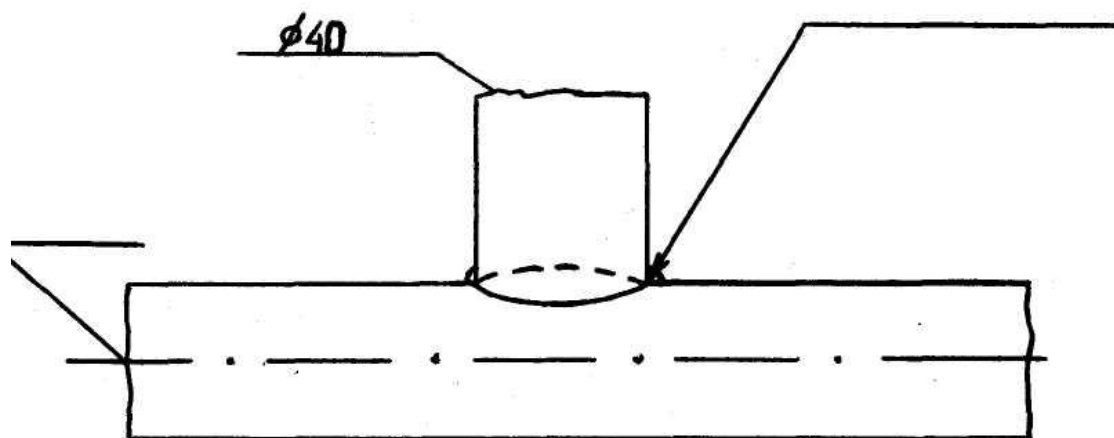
Эскиз сварного соединения труб под углом 90°
